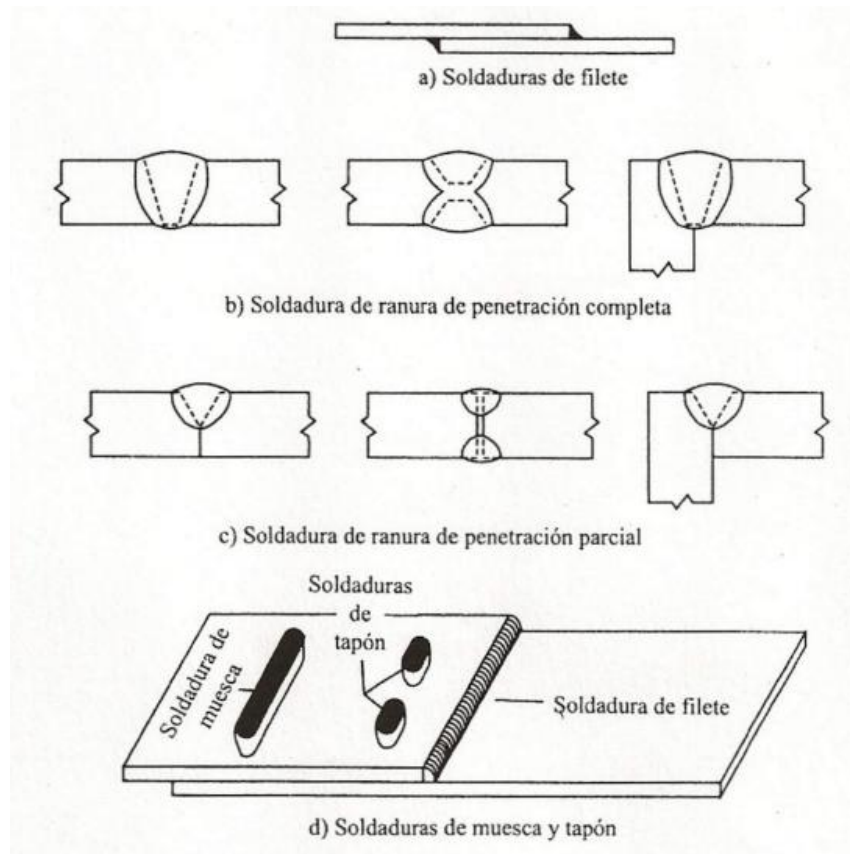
Tipos de soldadura. (Fuente: McCormac;2002;442)
